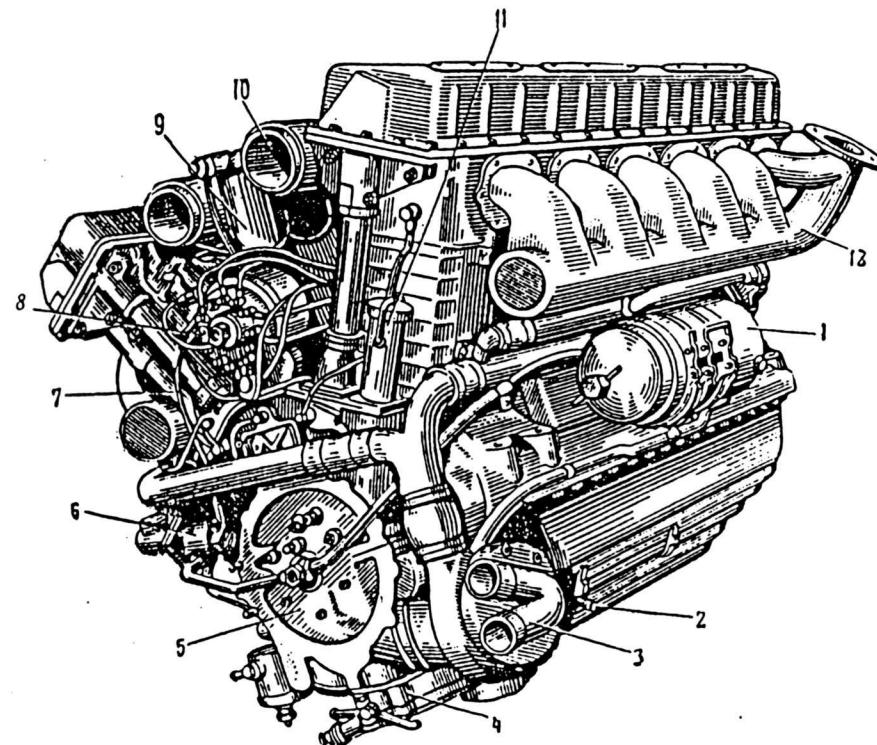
Двигатель В-54К-ИС (вид со стороны передач):
